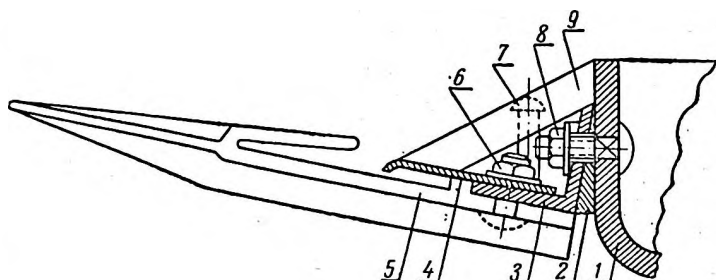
Крепление деталей переоборудованного режущего аппарата: 1 — передний брус; 2 — клиновидная подкладка; 3 — пальцевый брус; 4 — прижимная лапка; 5 — секция пальцев; 6, 7 — болты; 8 — болт с гайкой; 9 — деревянная накладка.
